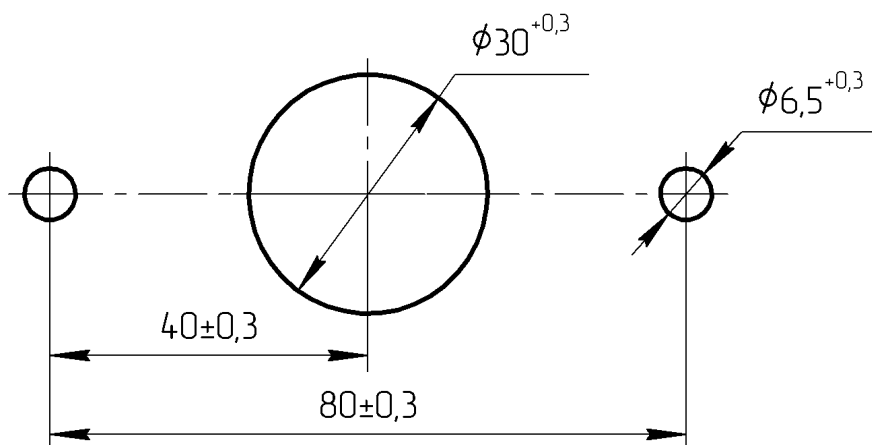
Разметка отверстий для монтажа блокиратора
